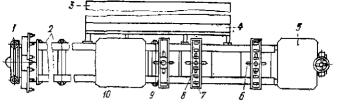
Стенд 13520 для сборки элементов трубопроводов: 1— устройство для пристыковки фланцев; 2—балки; 3—стол-иакопитель; 4— упор; 5—стол для установки отводов; 6—винтовая пара; 7—роли; 8, 9, 10— каретки.
